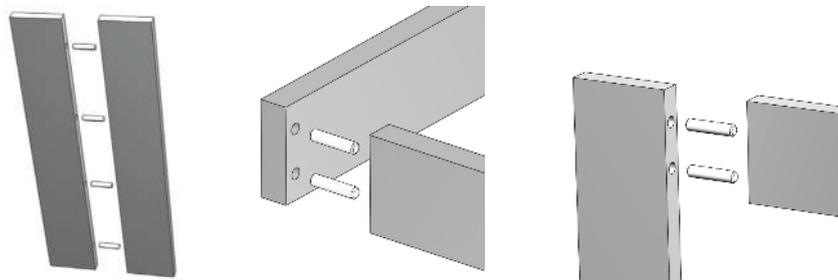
Exemplos de ligações com cavilhas de madeira
